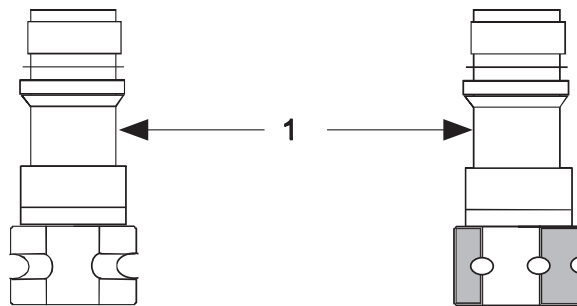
Корпуса датчика преобразователя GP серии 900 с двумя головками
